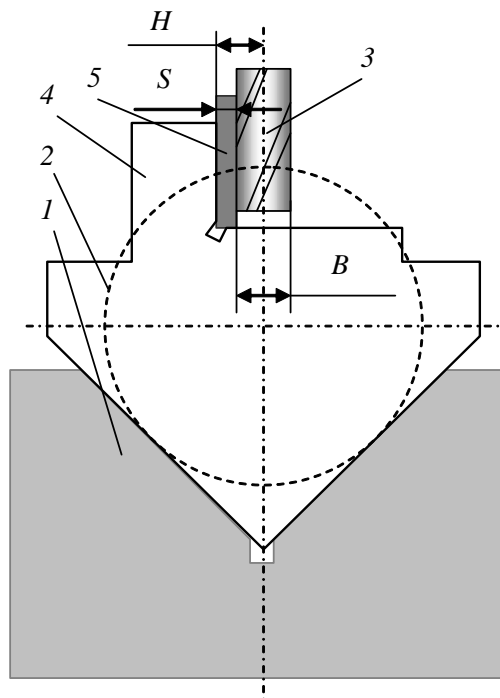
Схема налагодження для фрезерування шпонкового пазу
